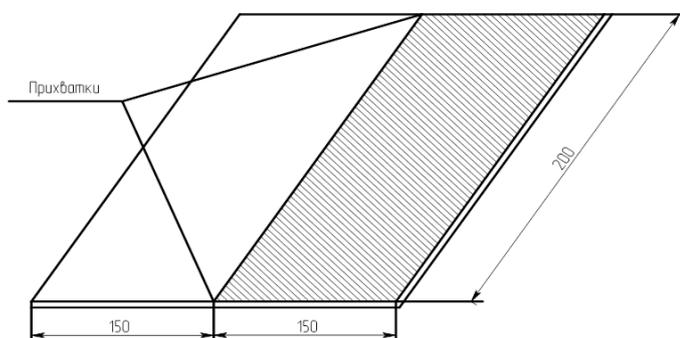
Схема сборки пластин для выполнения лабораторной работы
